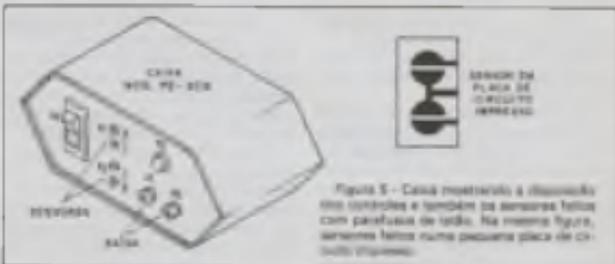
Caixa montada e dimensionada com controles e também as saídas feitas com perfis de ferro. Na mesma figura, sensores feitos numa pequena placa de circuito impresso.
